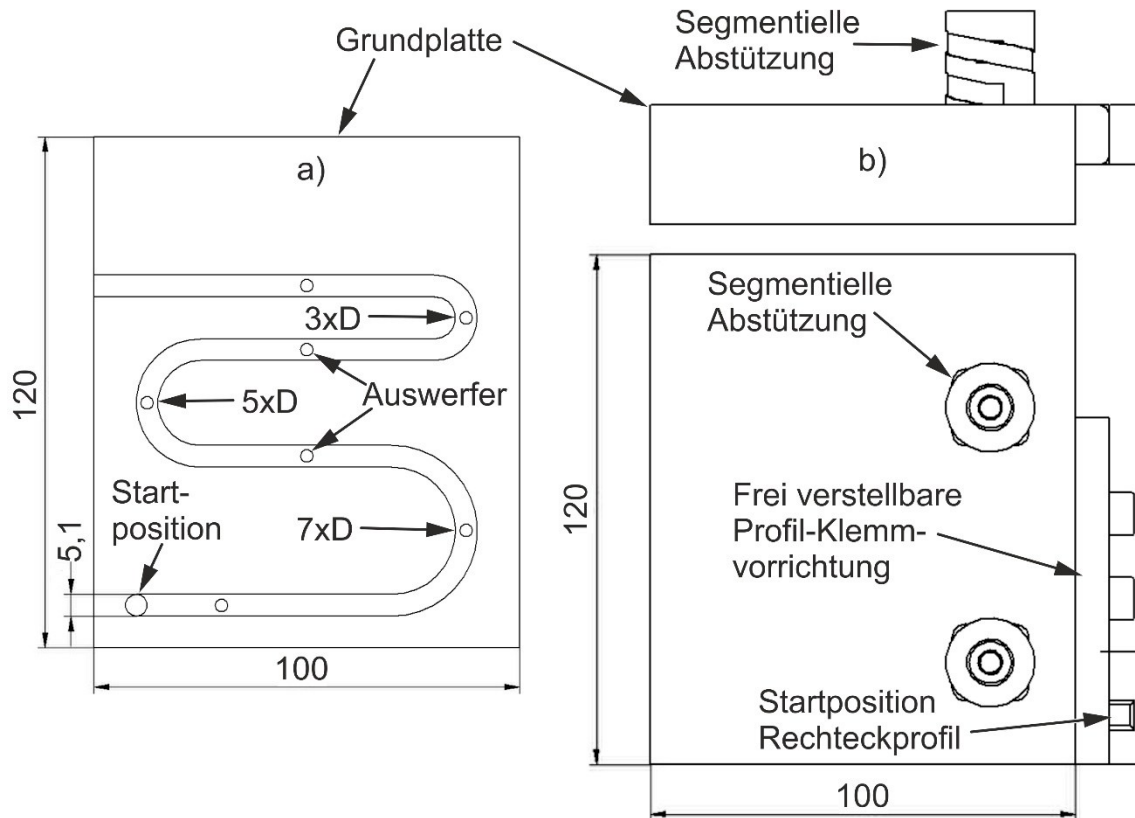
Werkzeugformarten und -aufnahme: a) Werkzeugform mit Nut, b) Werkzeugform mit segmentieller Abstützung
